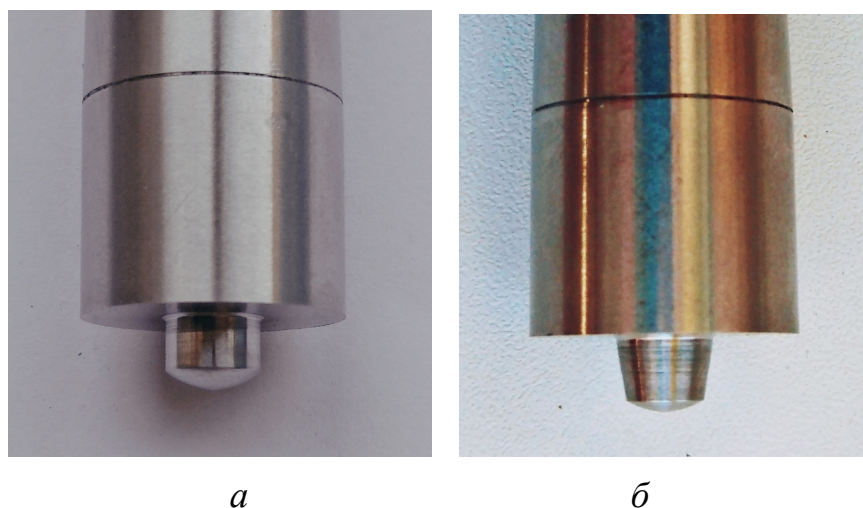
Форма пина инструмента для сварки трением с перемешиванием:
